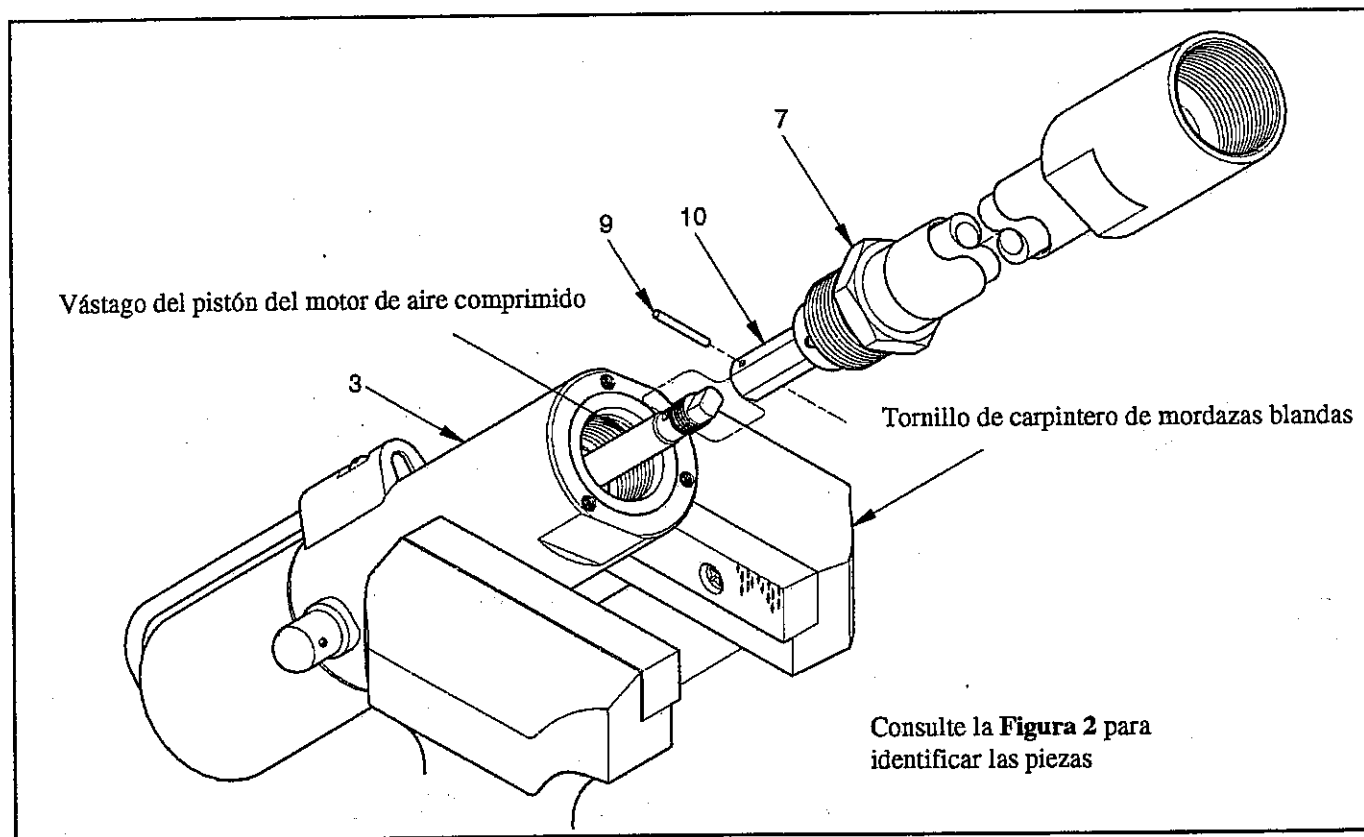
Separación del ensamblaje del tubo de bombeo del motor de aire comprimido
